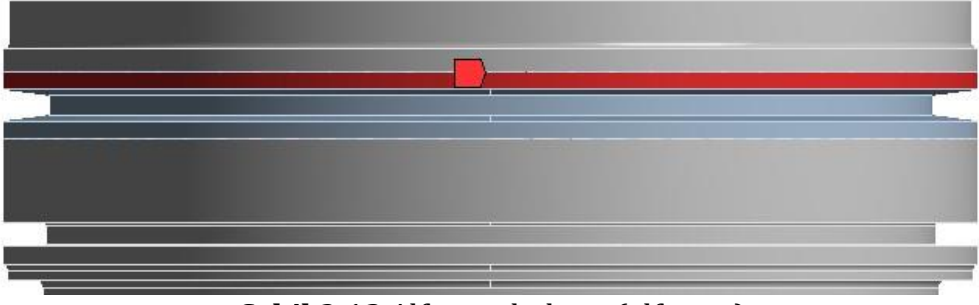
Piston üst yüzeyindeki büküm bölgesi (bowlrim)
